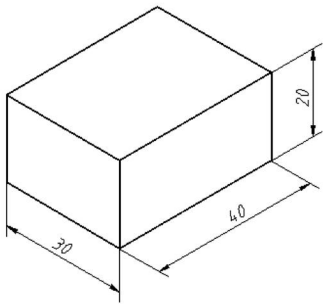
使用/ 编辑尺寸 0 调整尺寸界线方向
